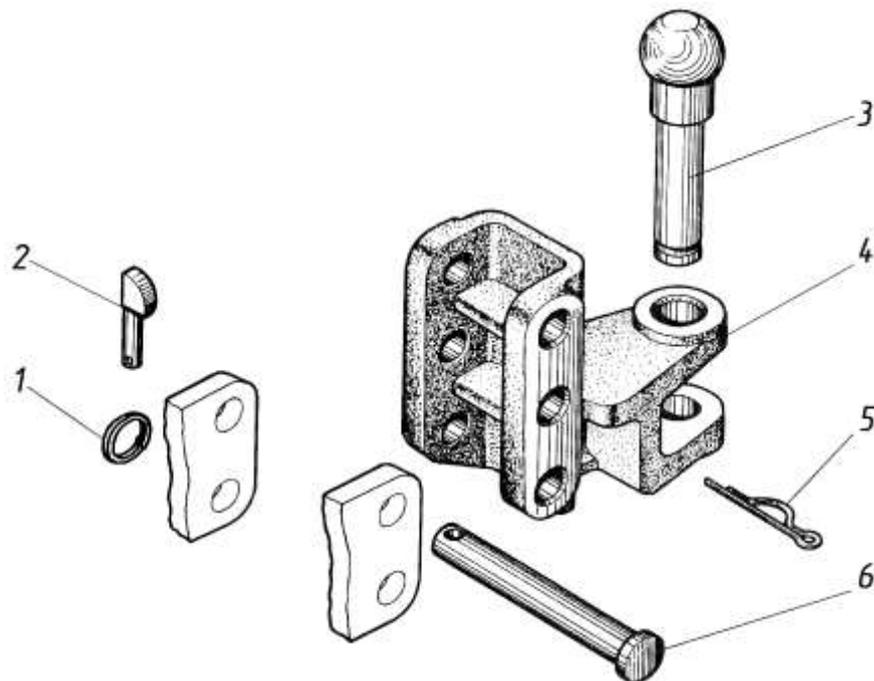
Тягово-сцепное устройство шарового типа
